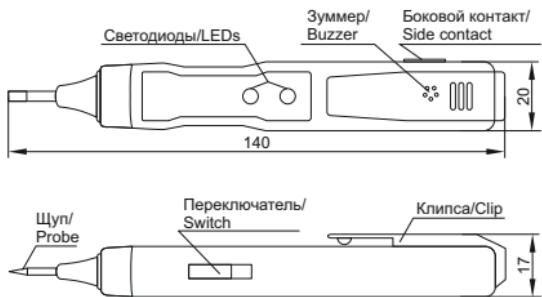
Габаритные размеры пробника / Figure1 – Overall dimensions of tester
